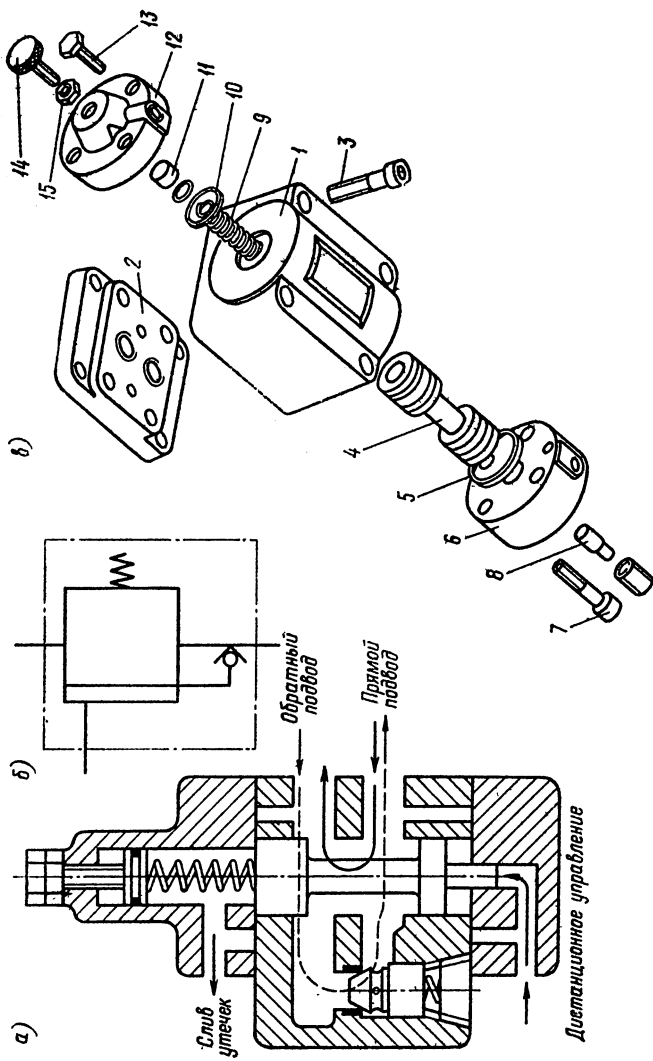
Сборка напорного золотника: а — схема золотника; б — условное обозначение; в — последовательность сборки
